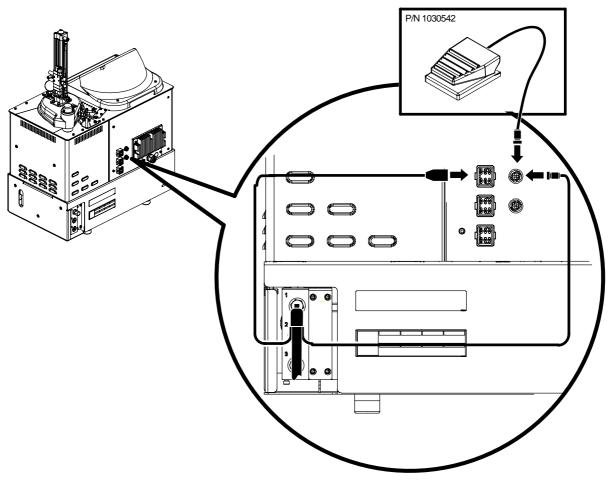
Schlauch für Handpistole mit Schalter oder Fußschalter anschließen
